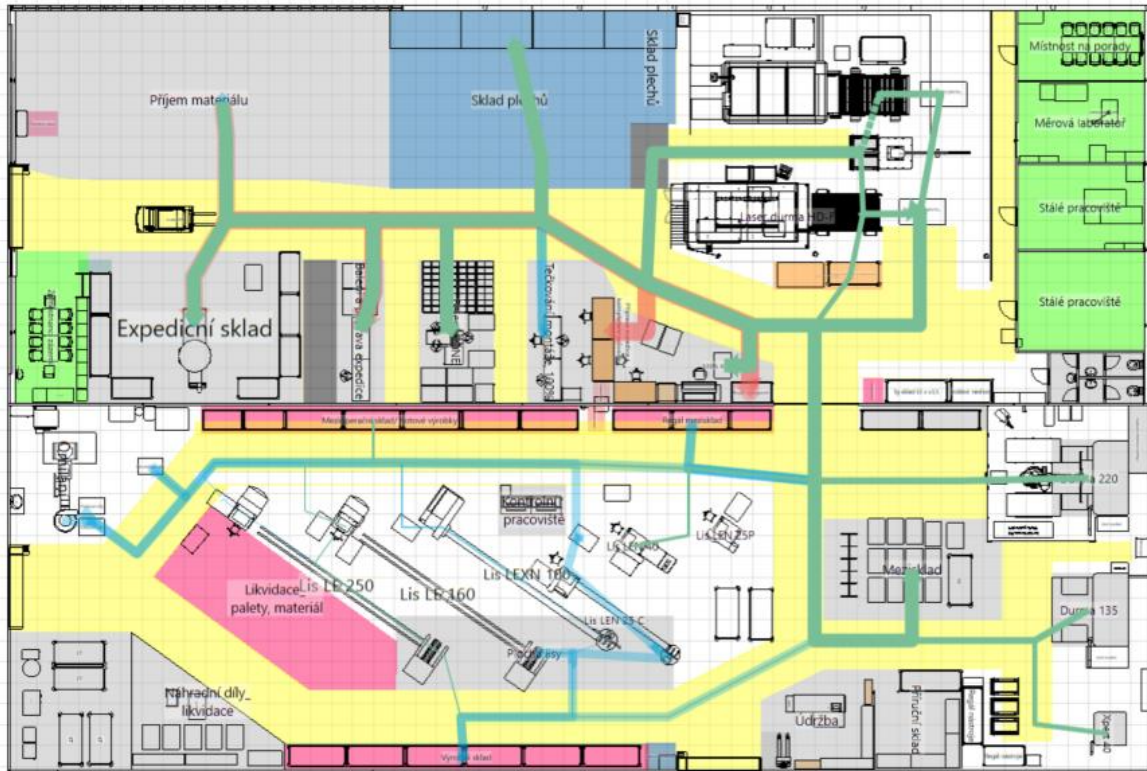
2D Layout haly včetně využitých ploch - Varianta 1
